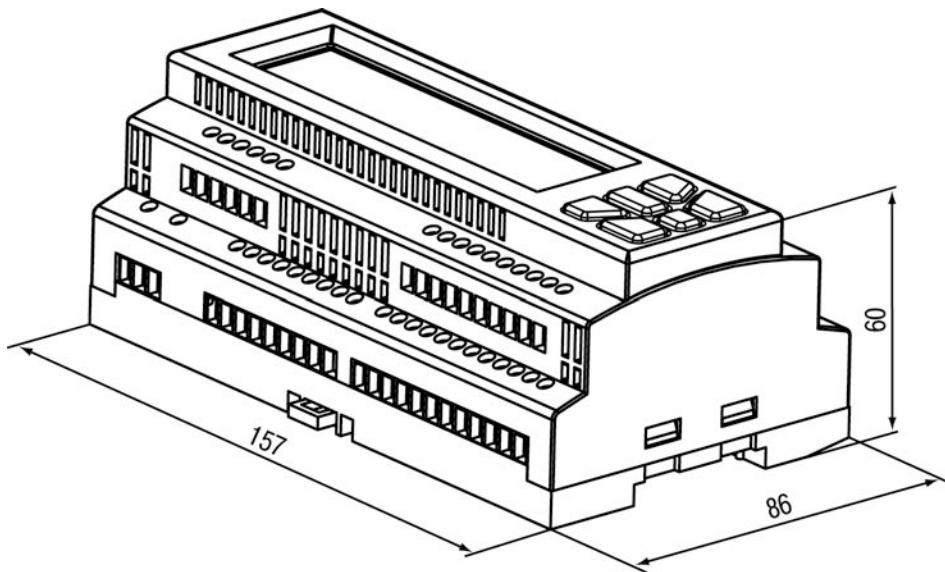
Корпус для крепления на DIN-рейку 35 мм
